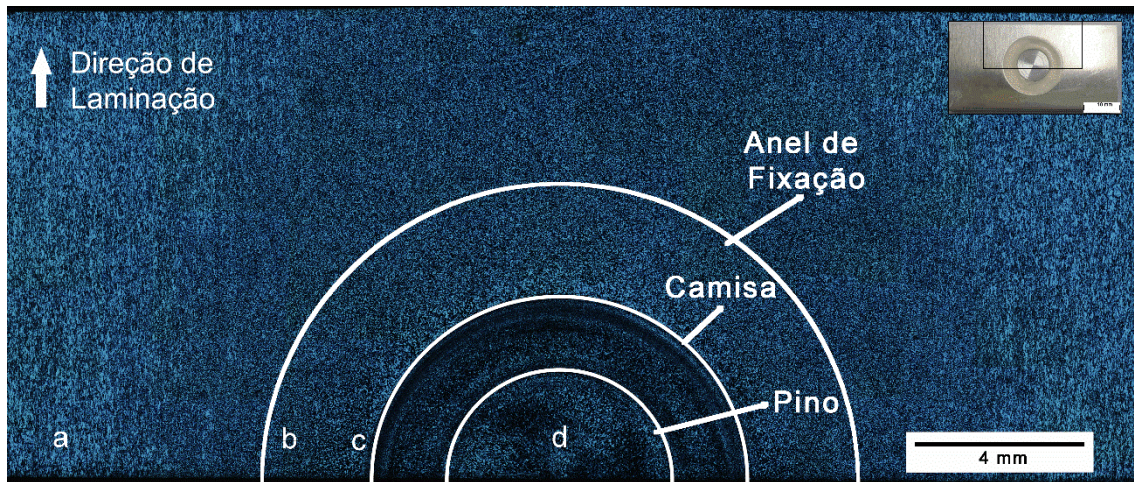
Imagem macroscópica da superfície da junta soldada AA5754-H22/Ti-6Al-4V.
